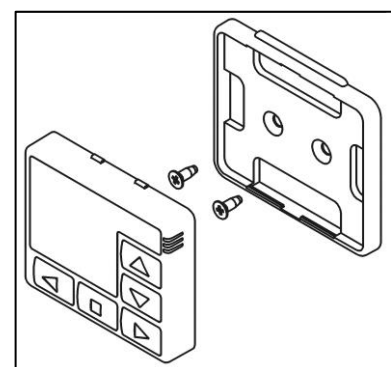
Montage des Bedienfeldes PU-27 mit einer Montagehalterung.
